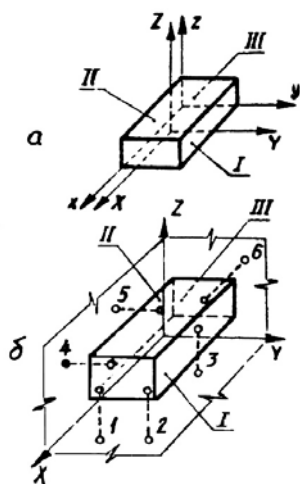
Комплект баз (а) и опорные точки (б) при базировании призматической заготовки (детали): I, II, III – базы; 1...6 – опорные точки, символизирующие двусторонние связи заготовки с системой координат
